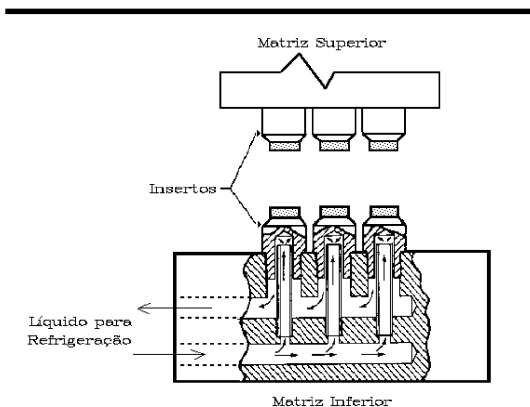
Exemplo de Solda por Projeção Múltipla.
